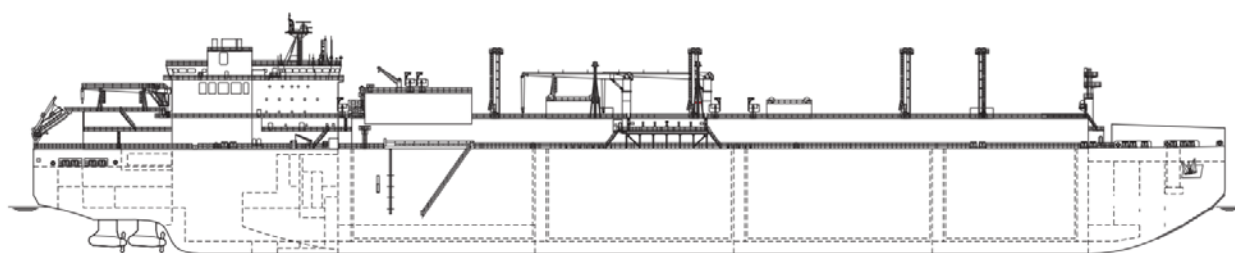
Схема корпуса газовоза класса Ямал МАКС
